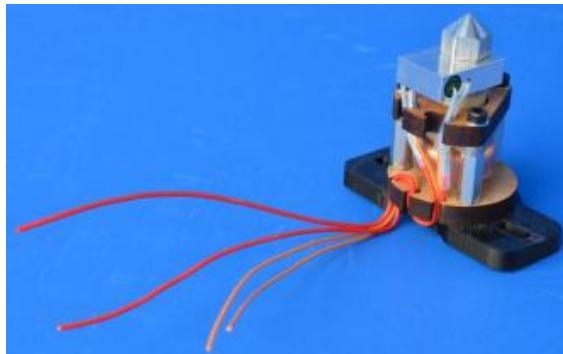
Colocación sobre el eje X y ensamblado del Hot-End (paso 1). Hot-End Budaschnozzle
